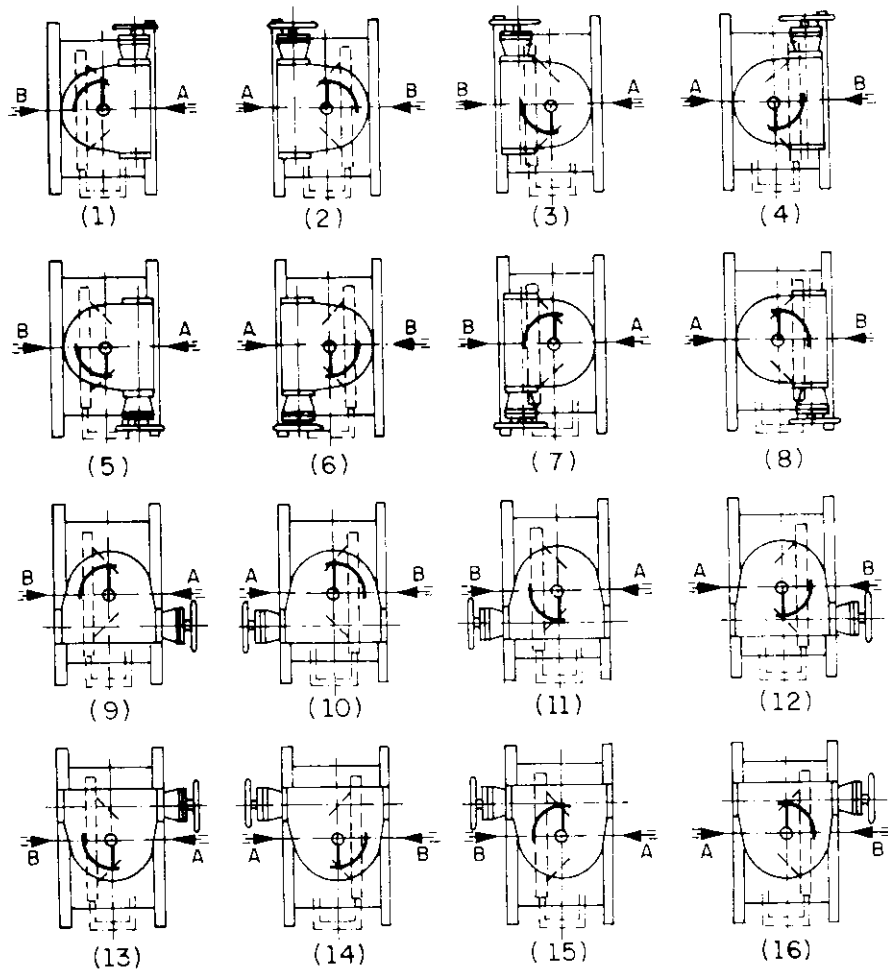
Posições possíveis de instalação de Válvulas Borboleta
